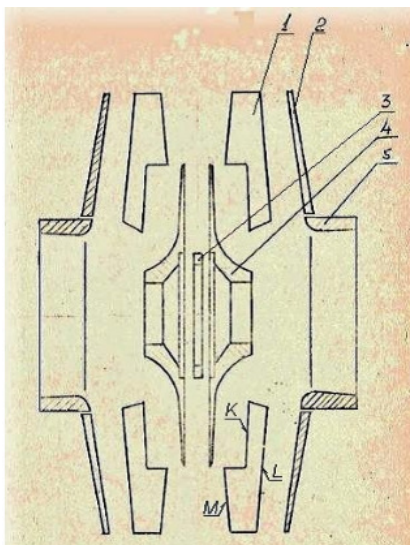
Составные части рабочего колеса сварной конструкции высоконапорного центробежного насоса
